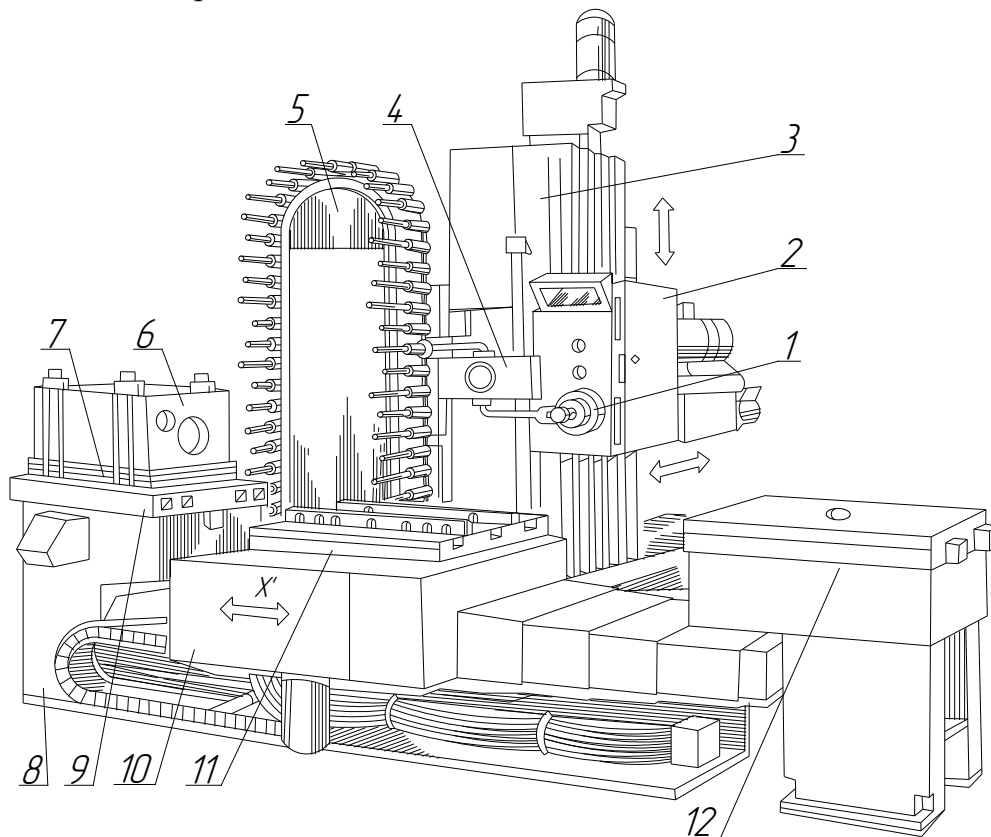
Горизонтальний багатоопераційний верстат
